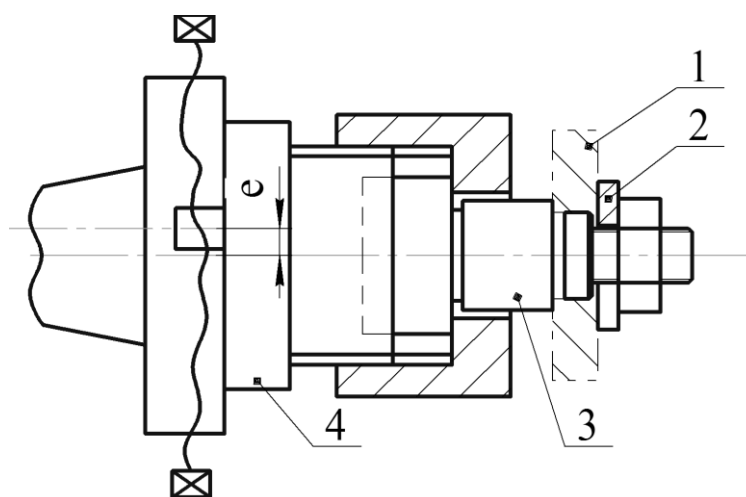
Групповая переналаживаемая оправка: 1 — заготовка; 2 — быстросъемная шайба; 3 — сменная наладка с различными посадками диаметра d ; 4 — ползушка, перемещаемая винтами 5
